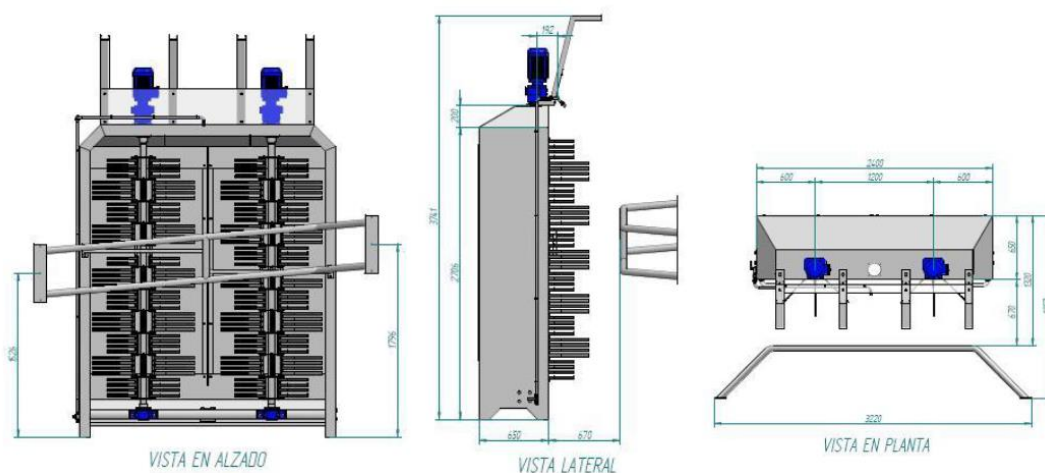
Vistas flageladora preescaldado (Mecanova, 2016).
